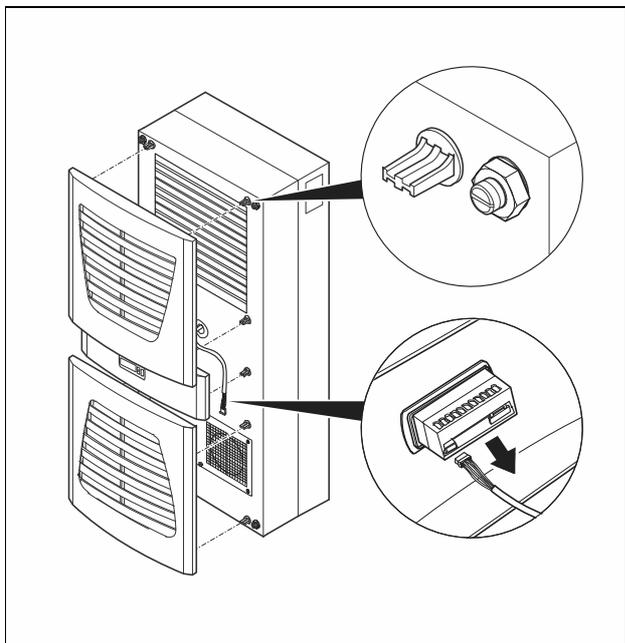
Remettre les grilles à lamelles en place et raccorder l'afficheur
